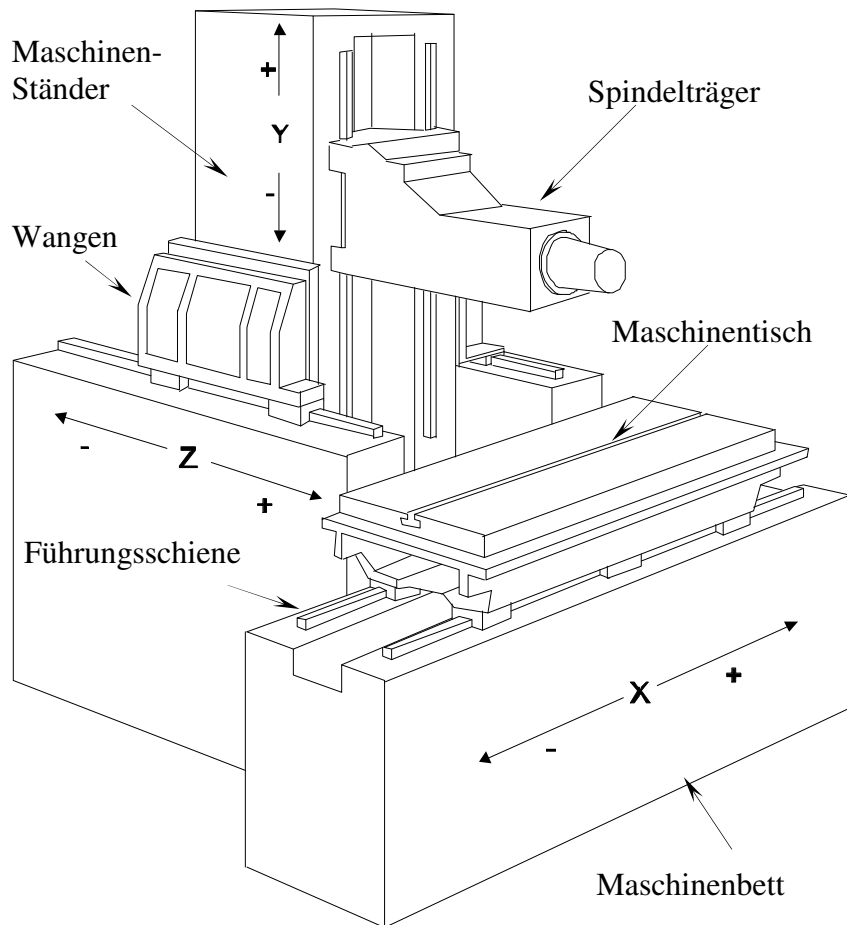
PLANOMAT Schleifmaschine Aufbau des Maschinenbettes mit Spindelträger, Linearführungen und Werkzeugmaschinentisch
